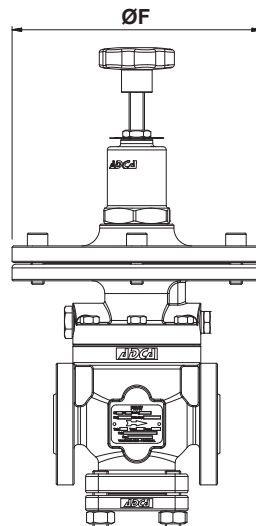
Ventil mit Niederdruck-Membrangehäuse
